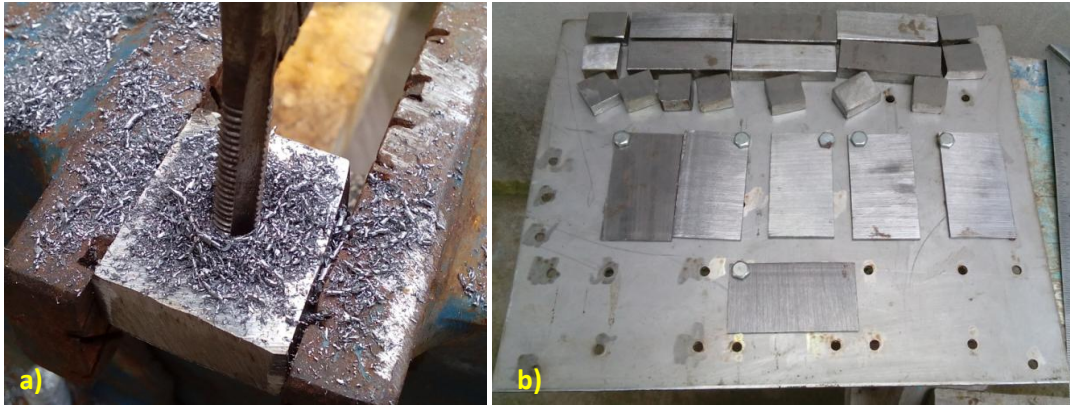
6. a) Perforado y machuelado de probetas para anclaje posterior, b) Probetas sujetas en placa previo al sandblasting
